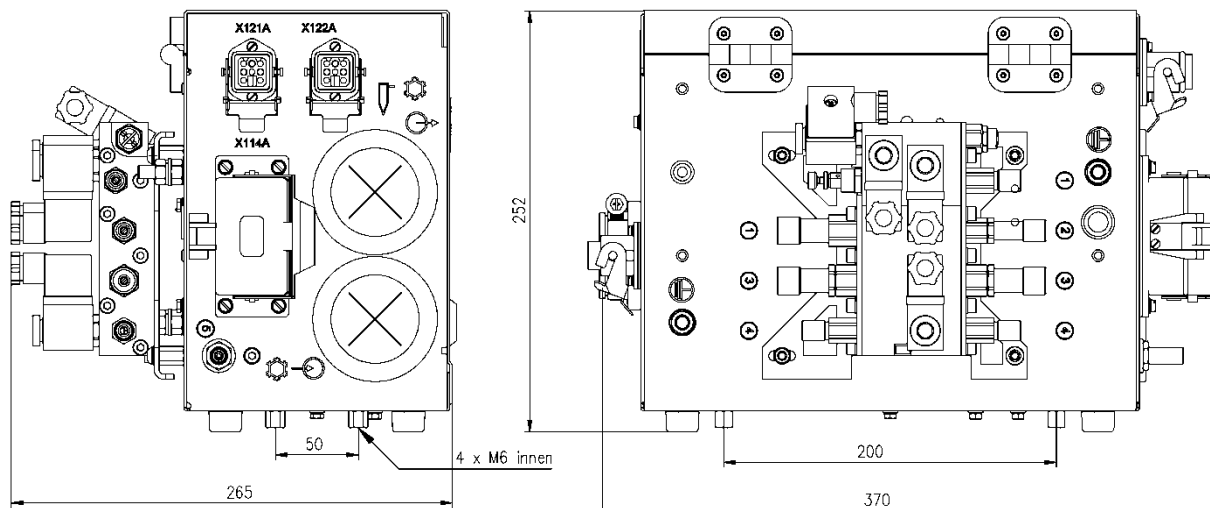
Чертеж с размерами подсоединительного блока для плазменной горелки PBA-440
